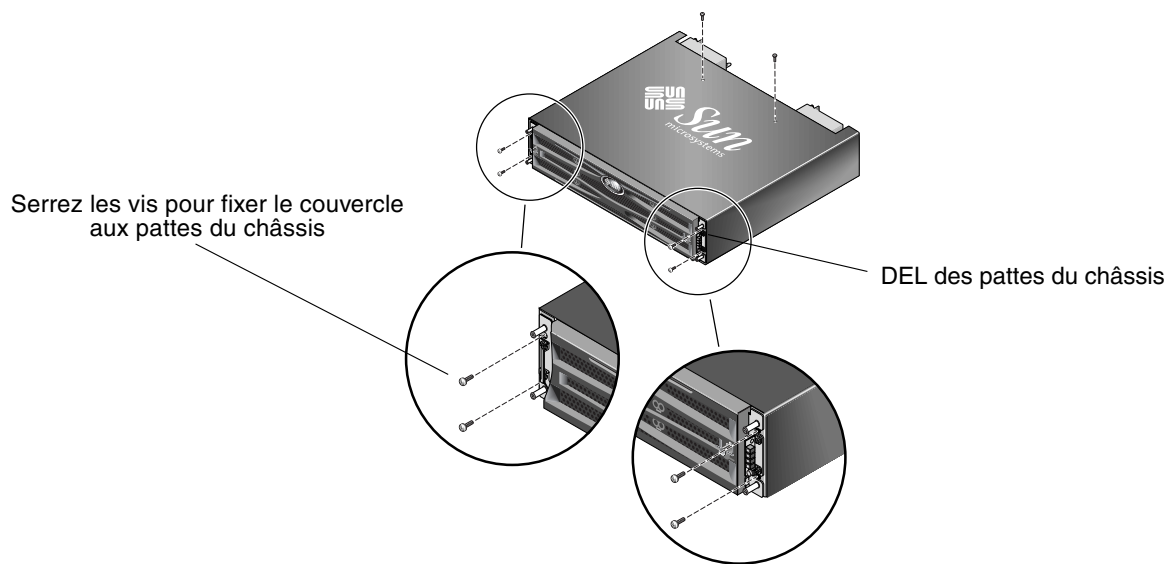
Fixation des pattes du châssis au couvercle de table
